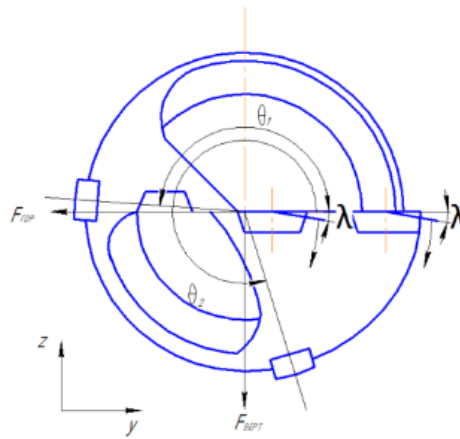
Одновременный поворот периферийной режущей пластины и центральной режущей пластины на  $-10^\circ$
